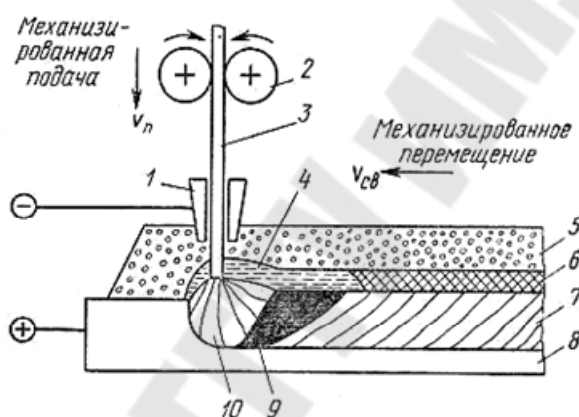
Схема автоматической дуговой сварки под флюсом
